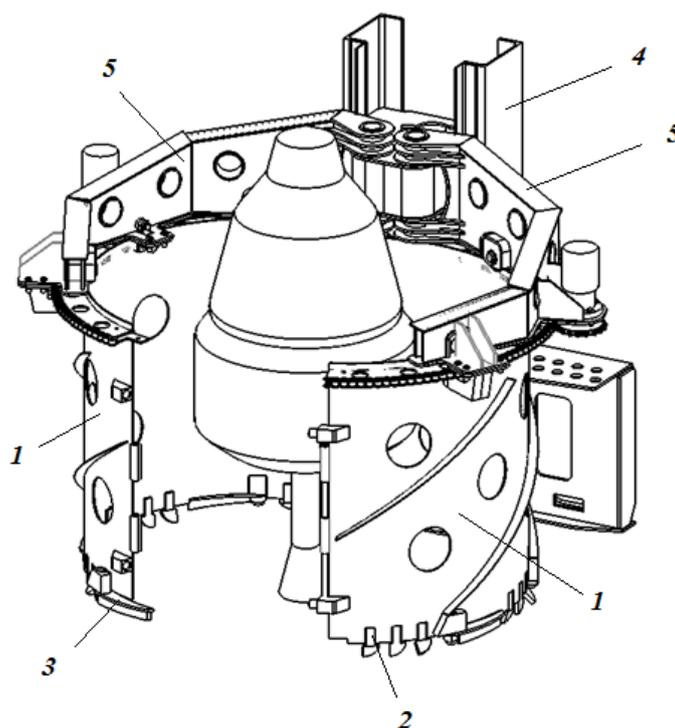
Навесное оборудование для пересадки деревьев из мерзлого грунта
